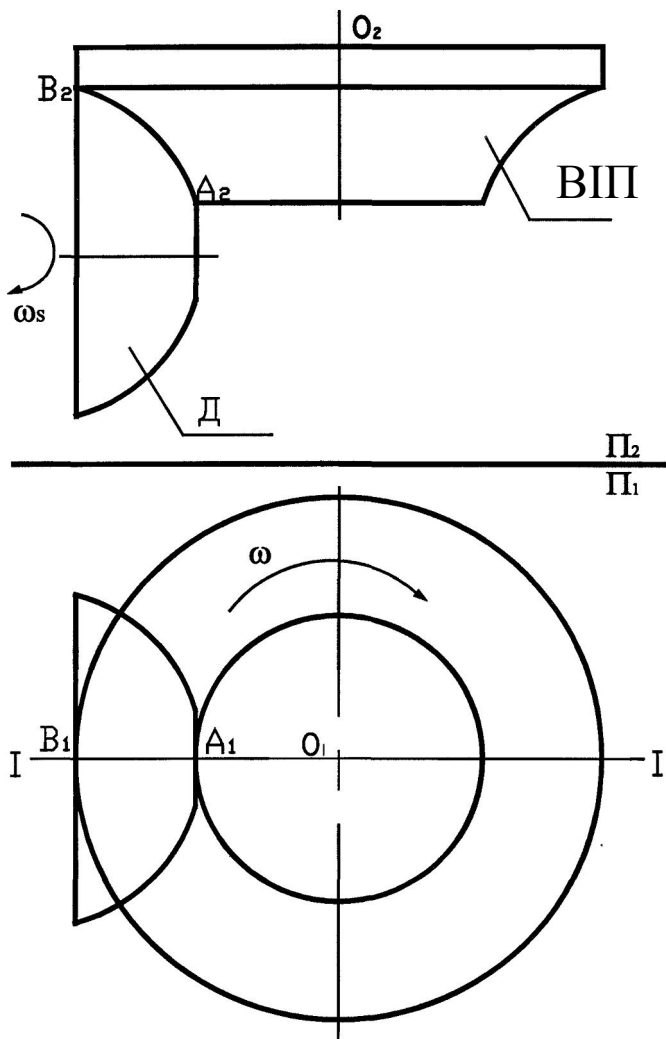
Кінематична схема оброблення торцевими фрезами поверхонь обертання
